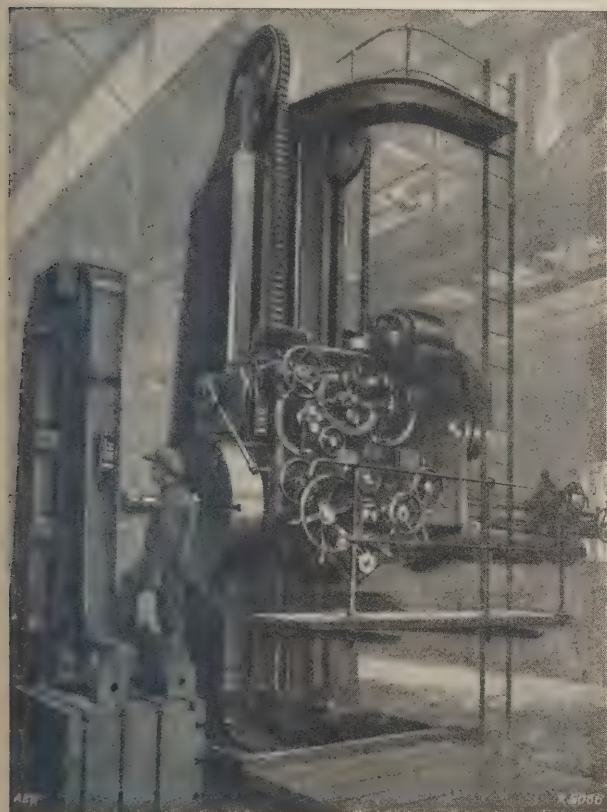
Horizontal-Bohr- und Fräsmaschine mit Reguliermotor und Druckknopfsteuerung beim Bearbeiten eines Walzenständers. (Maschinenfabrik Schieß-Defries, Düsseldorf.)
